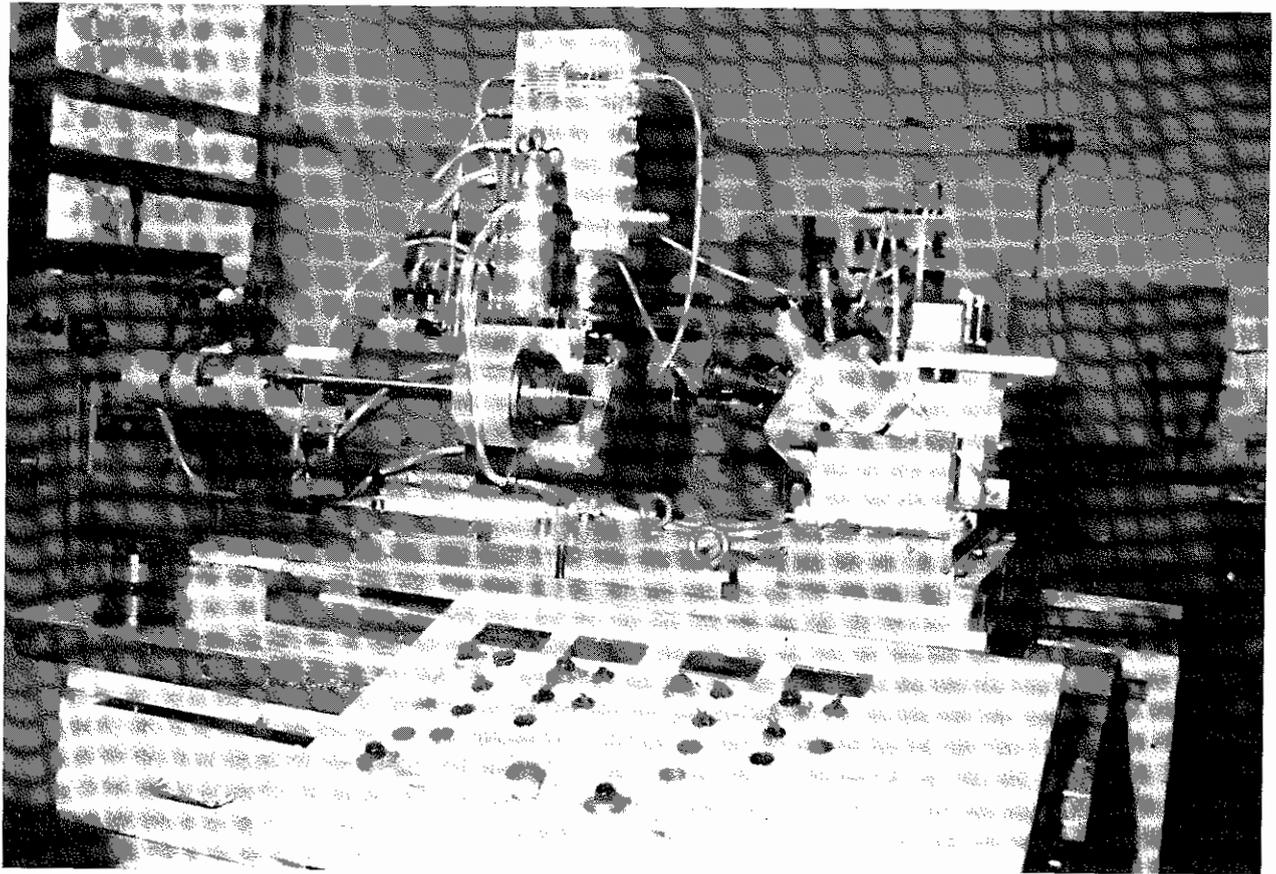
VUE D'ENSEMBLE MACHINE D'USINAGE
